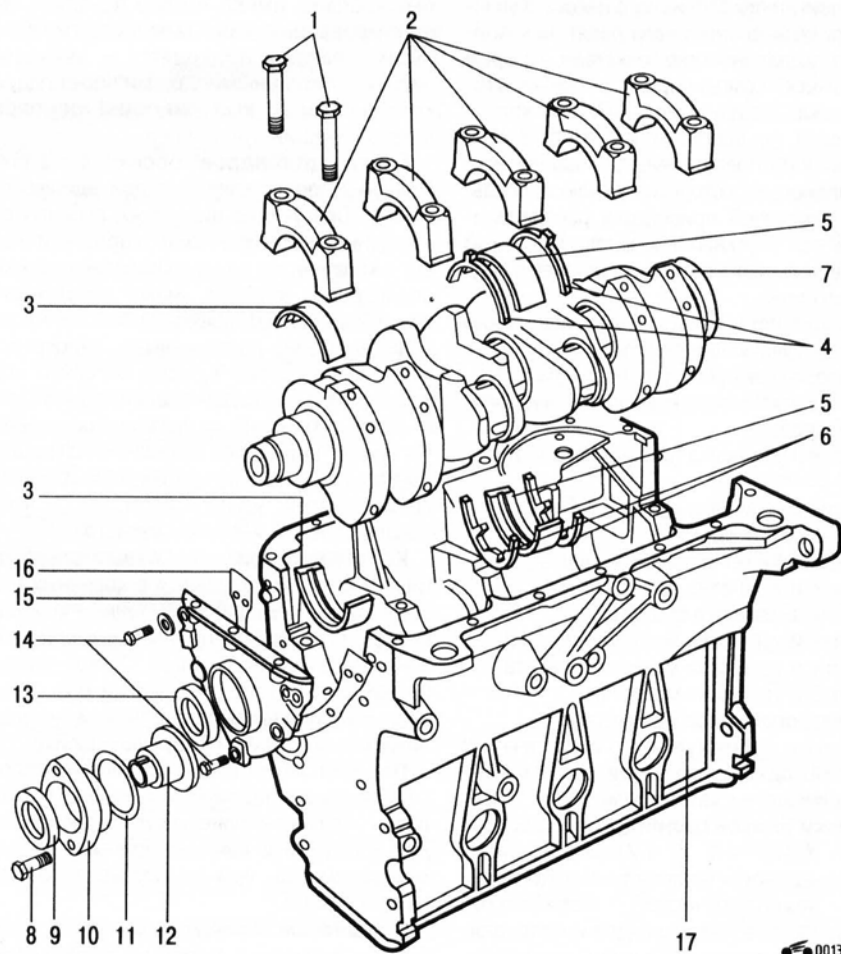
Блок цилиндров, коленчатый и промежуточный валы: 1 – болты крепления крышки коренного подшипника коленчатого вала; 2 – крышка коренного подшипника коленчатого вала; 3 – вкладыш коренного подшипника коленчатого вала; 4, 6 – упорные полукольца; 5 – вкладыш центрального (упорного) коренного подшипника коленчатого вала; 7 – коленчатый вал; 8 – болт крепления крышки промежуточного вала; 9 – сальник промежуточного вала; 10 – крышка промежуточного вала; 11 – уплотнительное кольцо промежуточного вала; 12 – промежуточный вал; 13 – передний сальник коленчатого вала; 14 – болты крепления передней крышки коленчатого вала; 15 – передняя крышка коленчатого вала; 16 – прокладка передней крышки коленчатого вала; 17 – блок цилиндров
